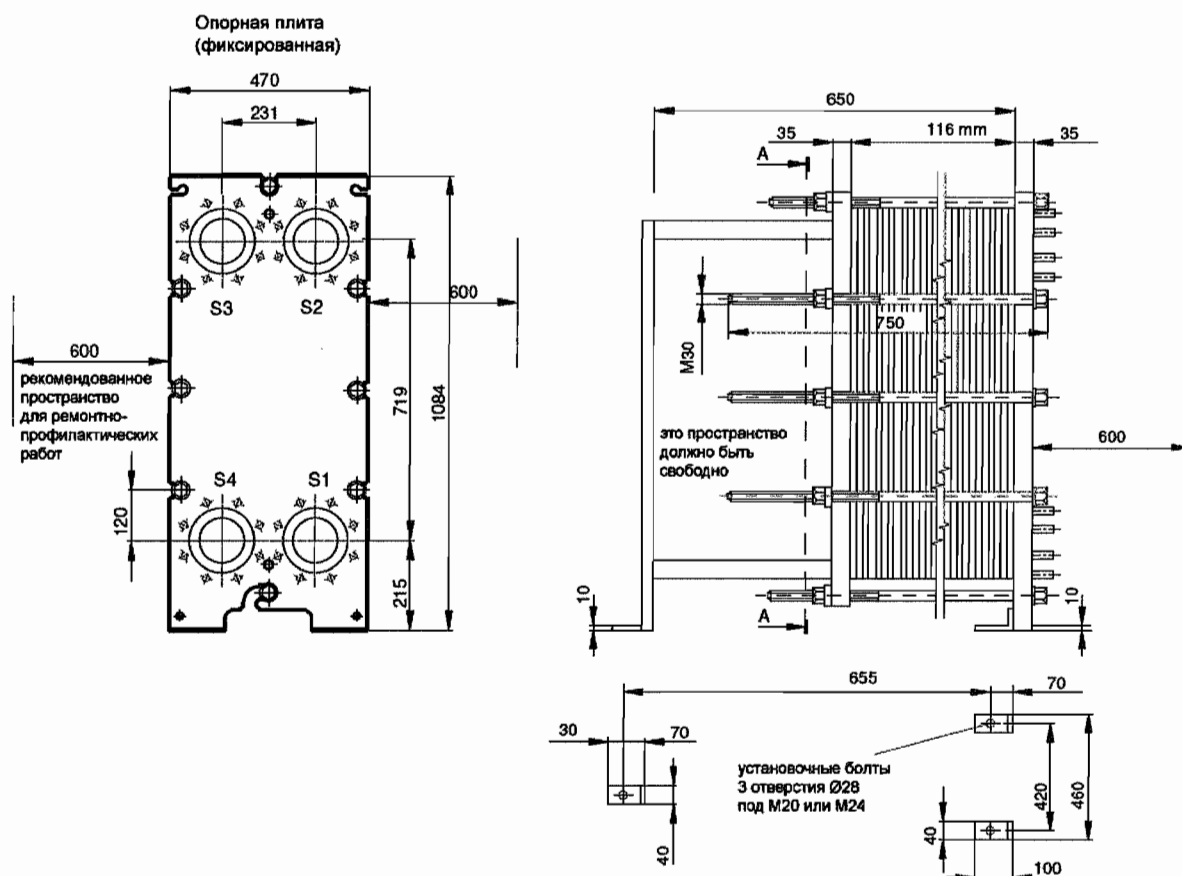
Габаритный чертеж охладителя конденсата KBF20AC001, KPF40AC001
